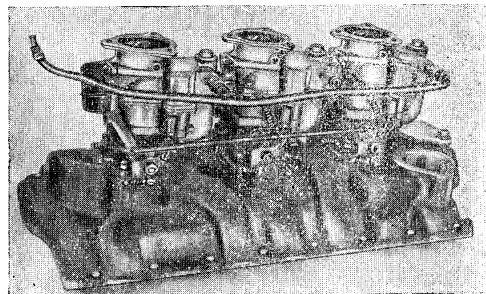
Карбюраторы и впускной трубопровод двигателя автомобиля ЗИЛ-112С
